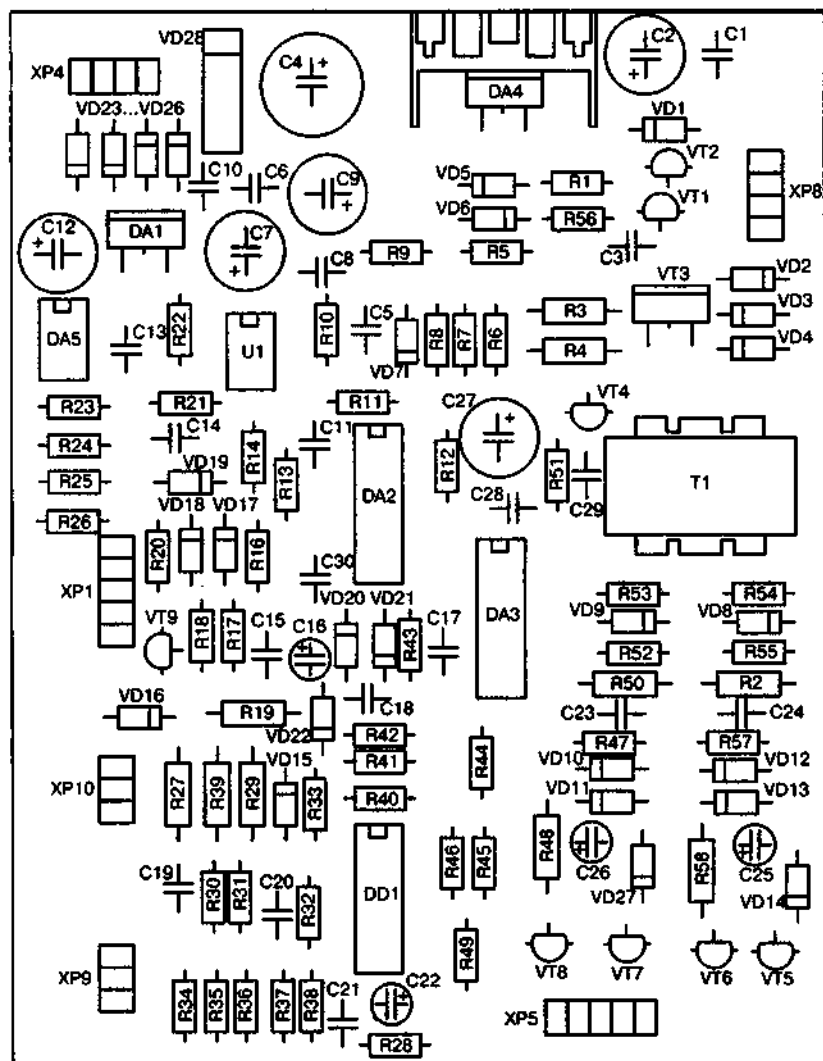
Расположение элементов на плате управления сварочного источника RANGER
